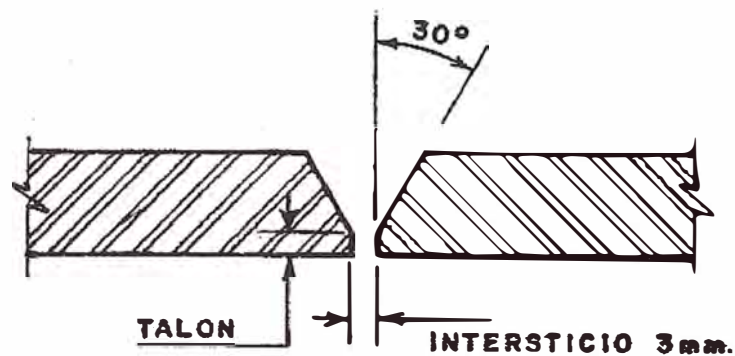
Esquema del diseño de junta para el soldeo del Tanque N 54
